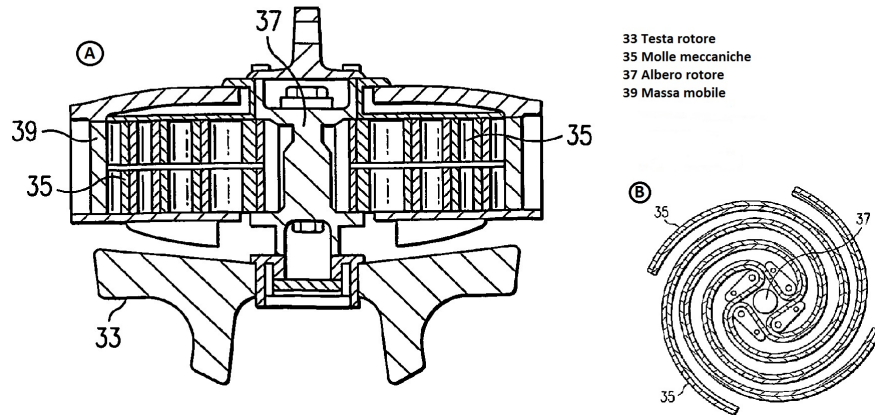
Sistema assorbimento vibrazioni 4 A) Sezione trasversale B) Vista dall'alto
